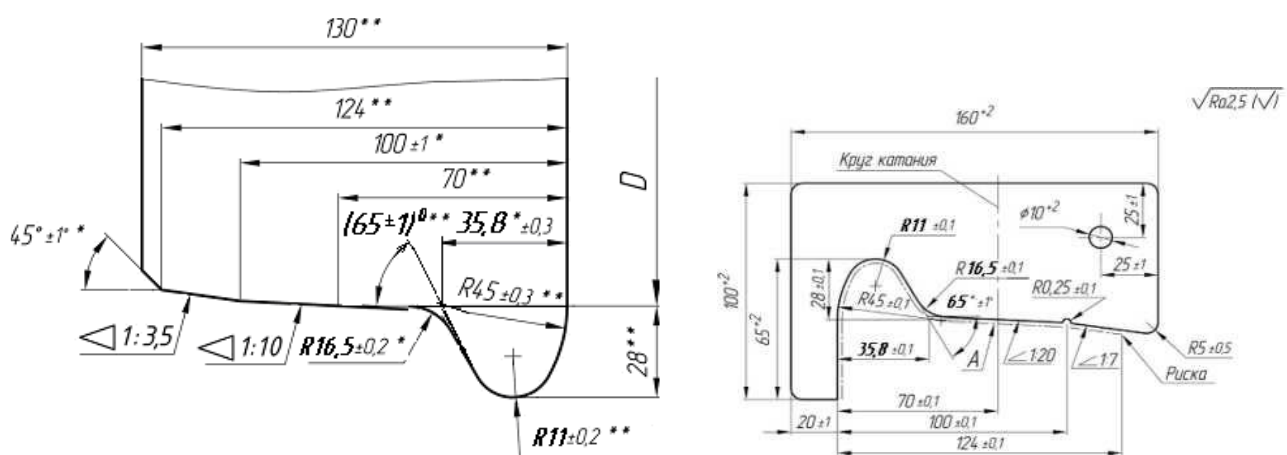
Профіль поверхні катання колеса ремонтний з вихідною товщиною гребеня 30,0 мм та максимальний шаблон для його перевірки
